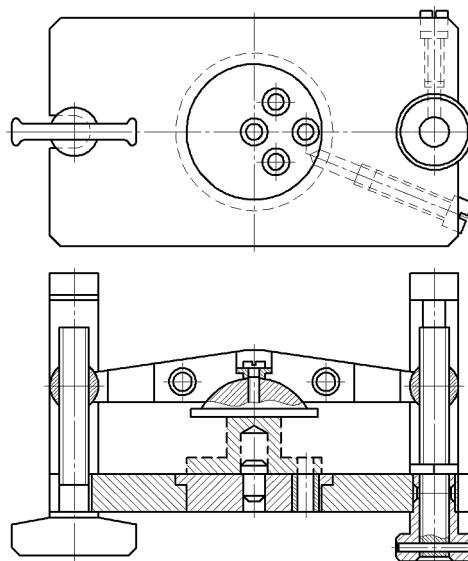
Групповой кондуктор для сверления отверстий во фланцах
